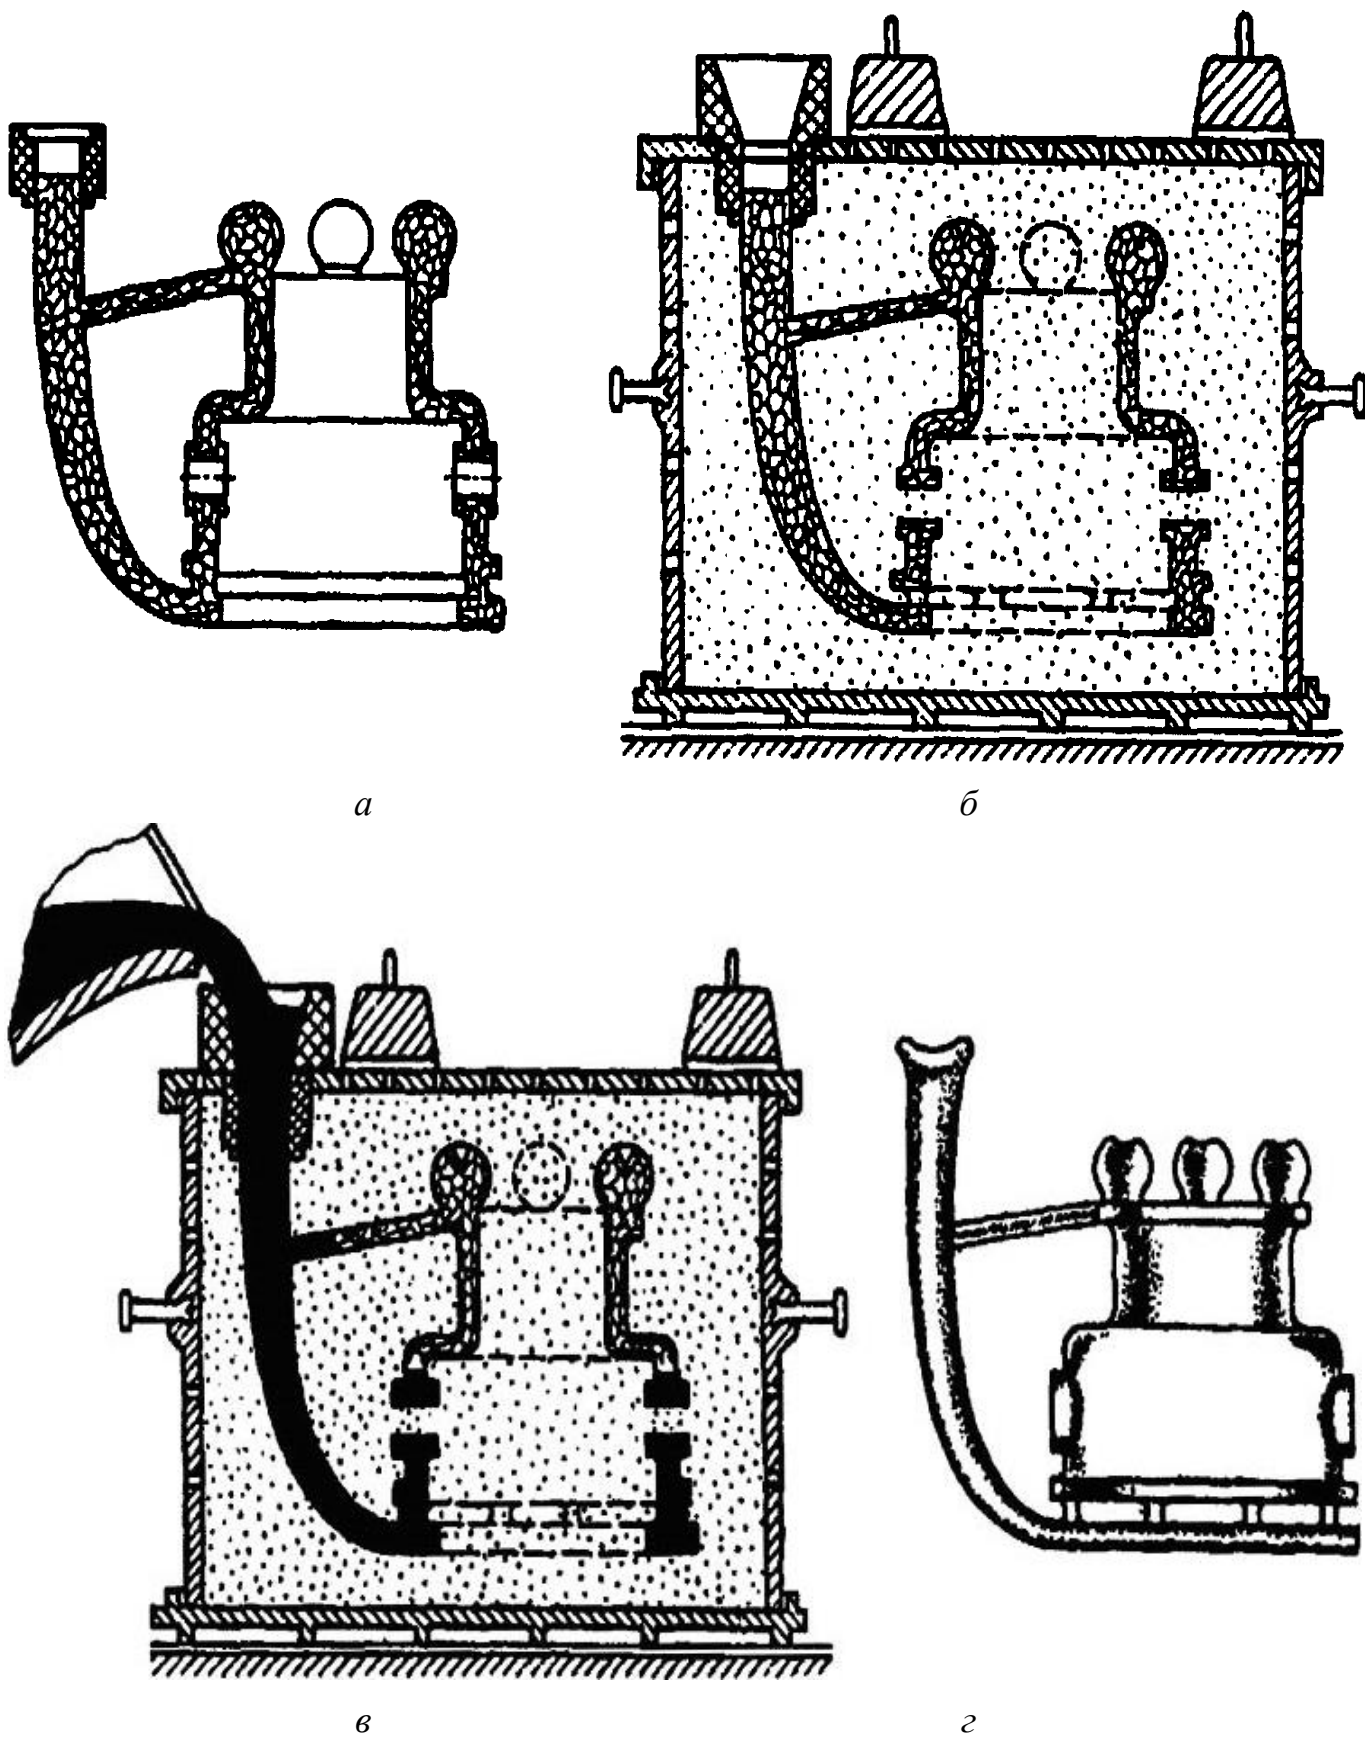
Схема виготовлення виливка за ЛГМ-процесом [221]:
